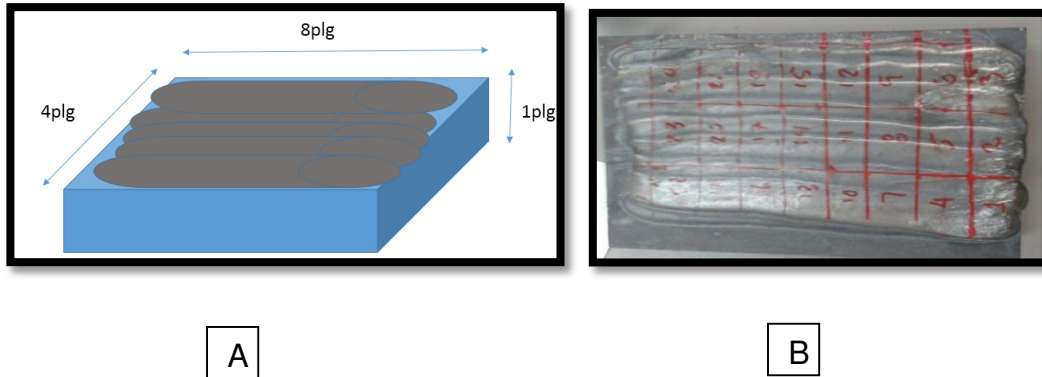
testigo de soldadura .A diseño para la aplicación de la soldadura , B después de la aplicación de cladding y rallado para testigos de soldadura
